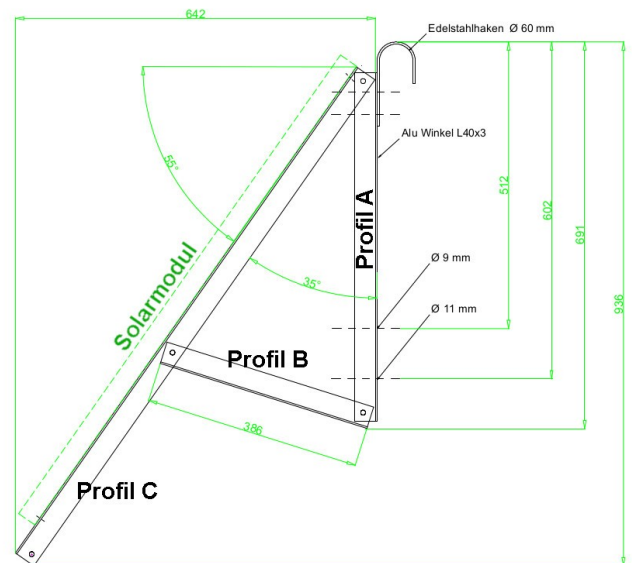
Ansicht des Dreiecks mit 35°-Neigung. Das Solarmodul wird rückseitig an das Profil C geschraubt. Optional kann es auch geklemmt werden.
